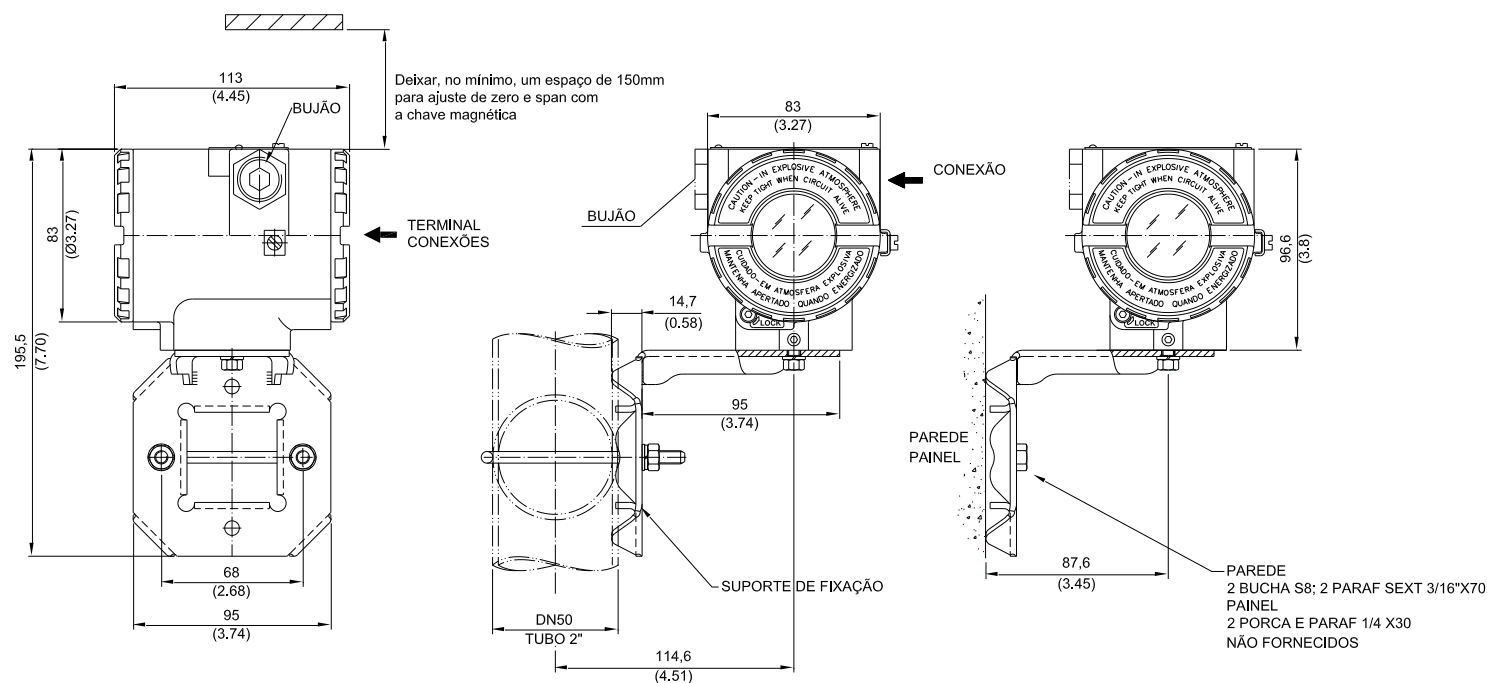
Desenho Dimensional e Posições de Montagem
